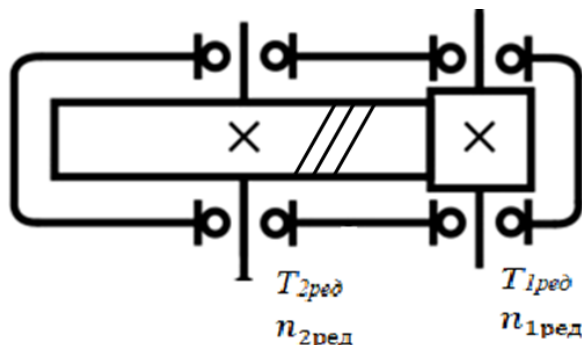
Кінематична схема циліндричного косозубого одноступеневого редуктора
